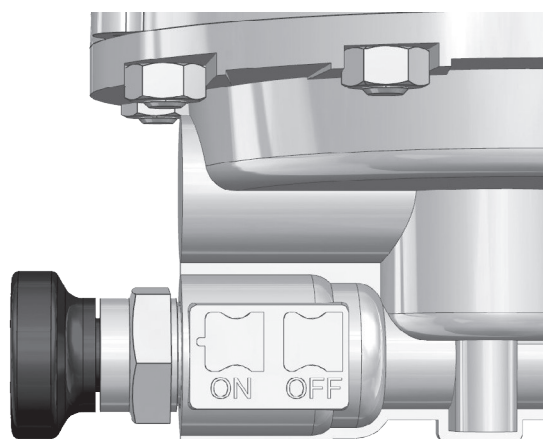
Zaaretování Mechanismu Řídící Jednotky
